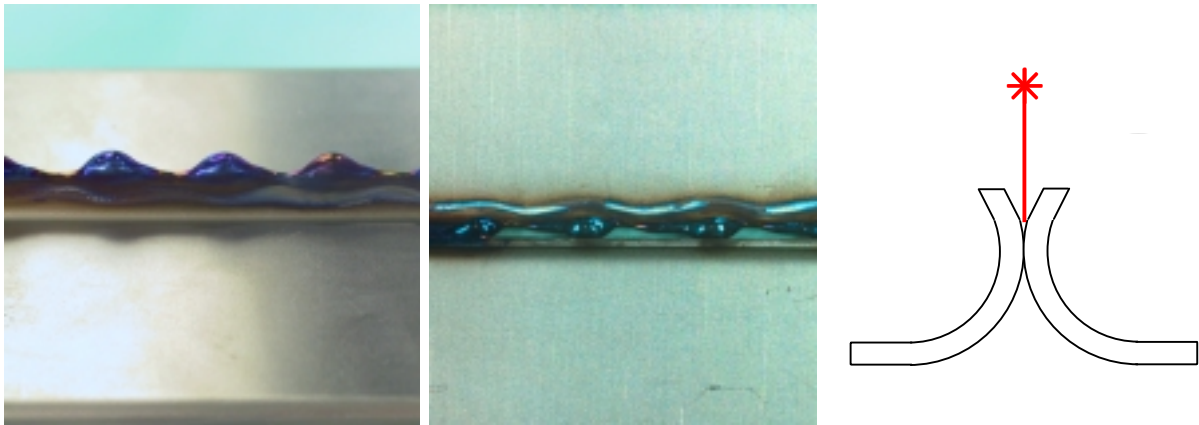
Imperfeições no cordão de solda (esquerda) e excesso de curvamento (direita).
